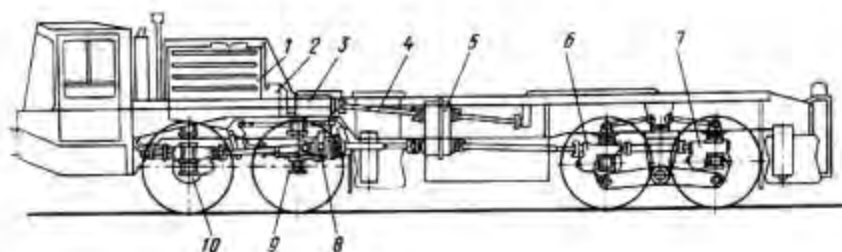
Схемы компоновки трансмиссии четырехосного специального шасси автомобильного типа. 1 – двигатель, 2 – сцепление, 3 – коробка передач, 4 – карданный вал, 5 – раздаточная коробка, 6 – приводной мост с двухступенчатой цилиндрической главной передачей, 7 – приводной мост, 8 – промежуточная опора, 9 – управляемый мост, 10 – управляемый приводной мост
